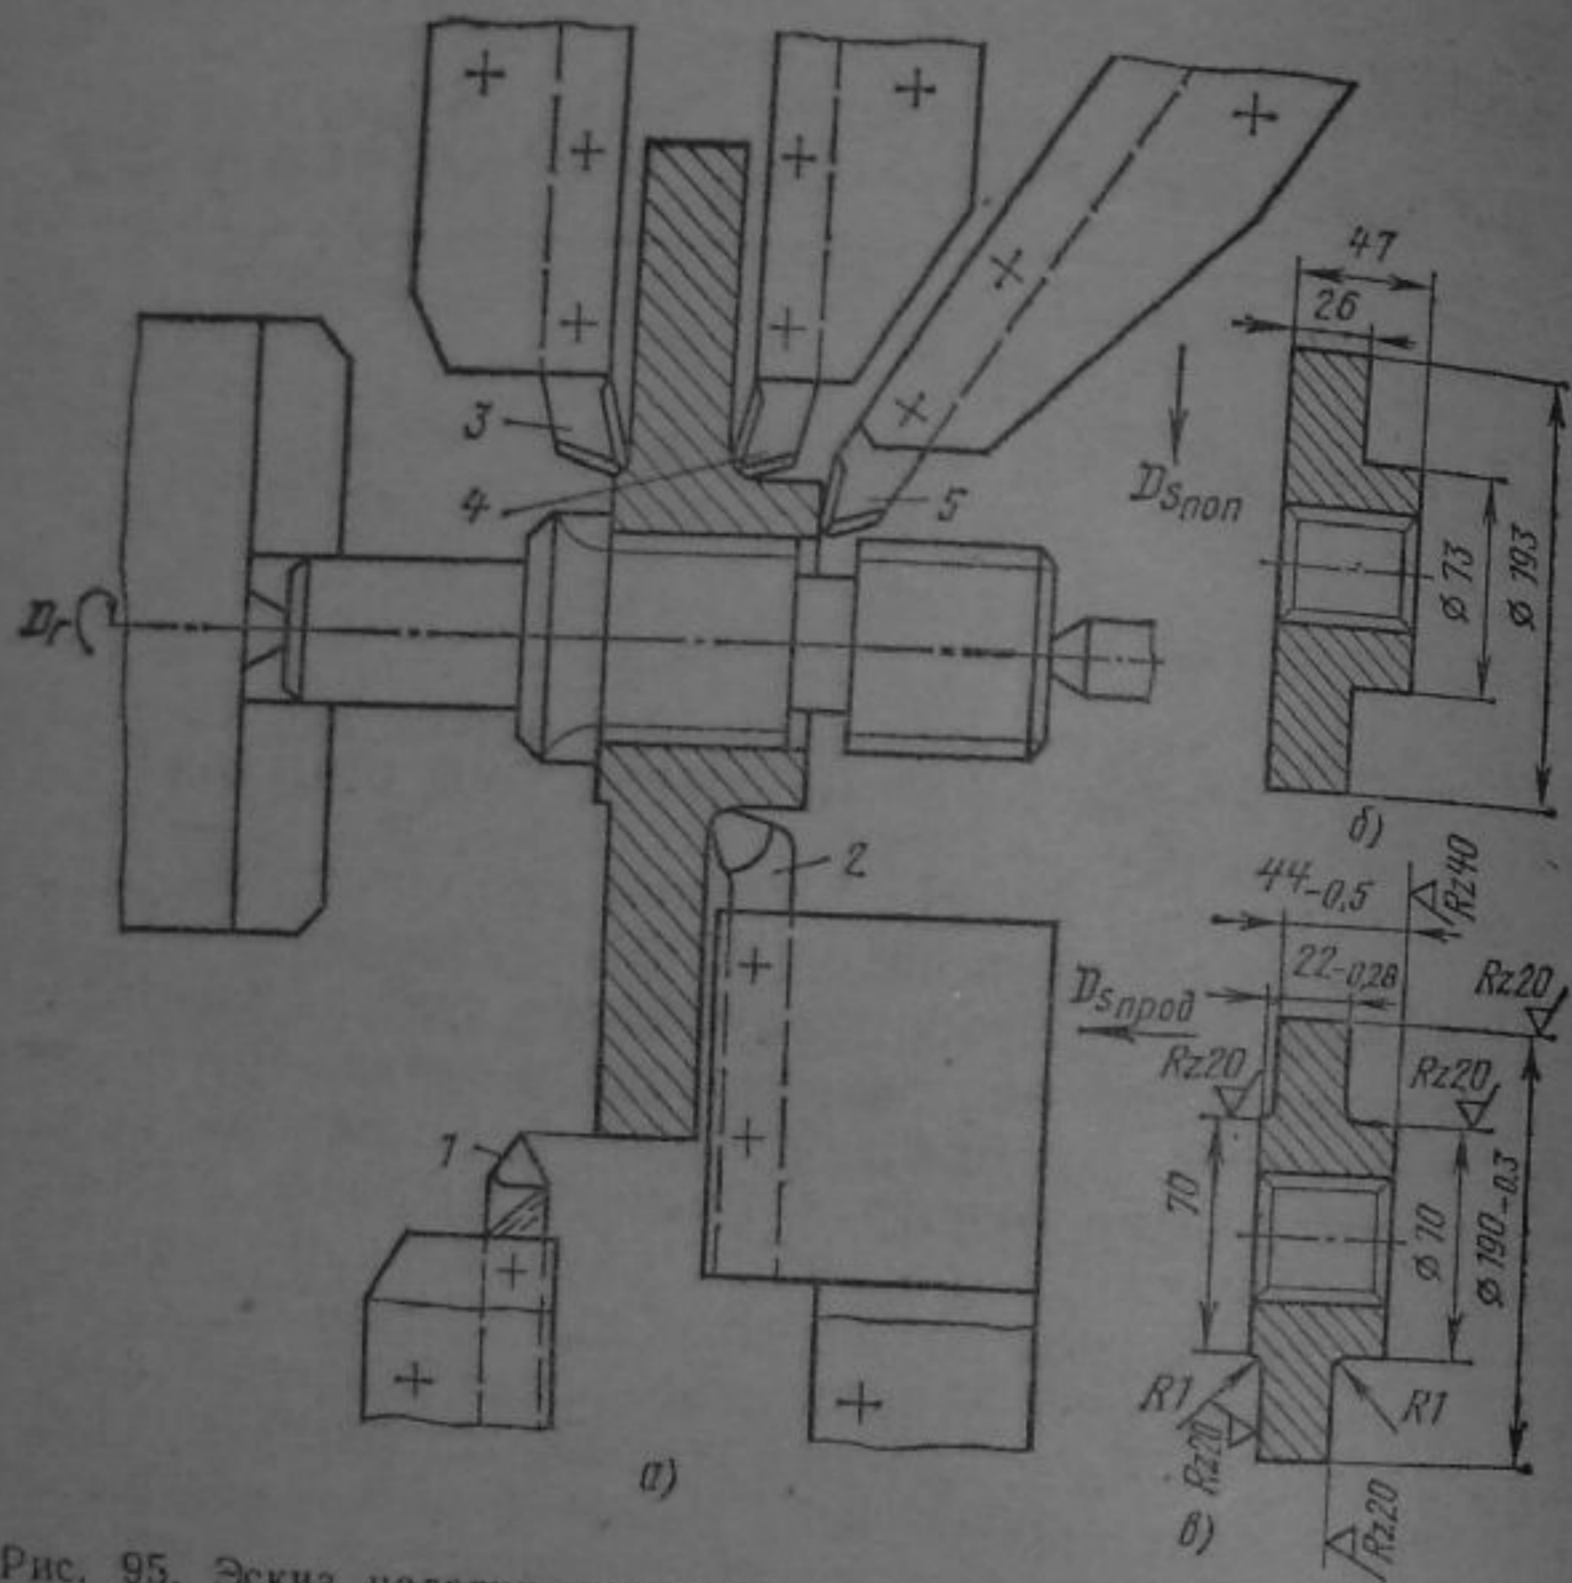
Эскиз наладки токарного одношпиндельного полуавтомата для обработки зубчатого колеса:
